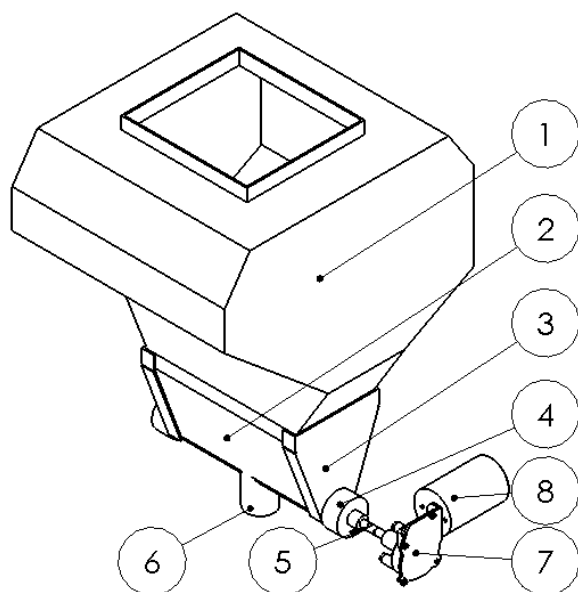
Componentes del dosificador de Fertilizantes. 1 - Tolva; 2 - carcasa del sin fin; 3 - tapa lateral de la carcasa; 4 - Rodamiento del sin fin; 5 – Flecha del sin fin; 6 – Descarga; 7 – Reductor del motor y 8 – Motor de corriente directa.
